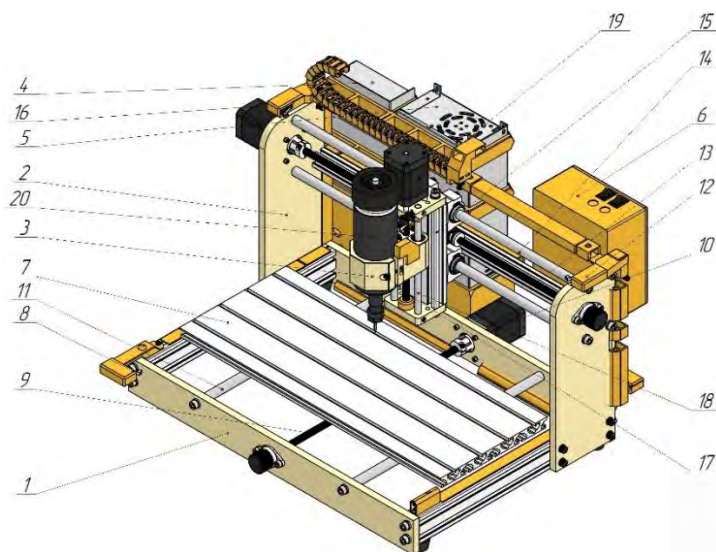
Фрезерно-гравірувальний верстат з ЧПК (CNC 3018-Plus)
